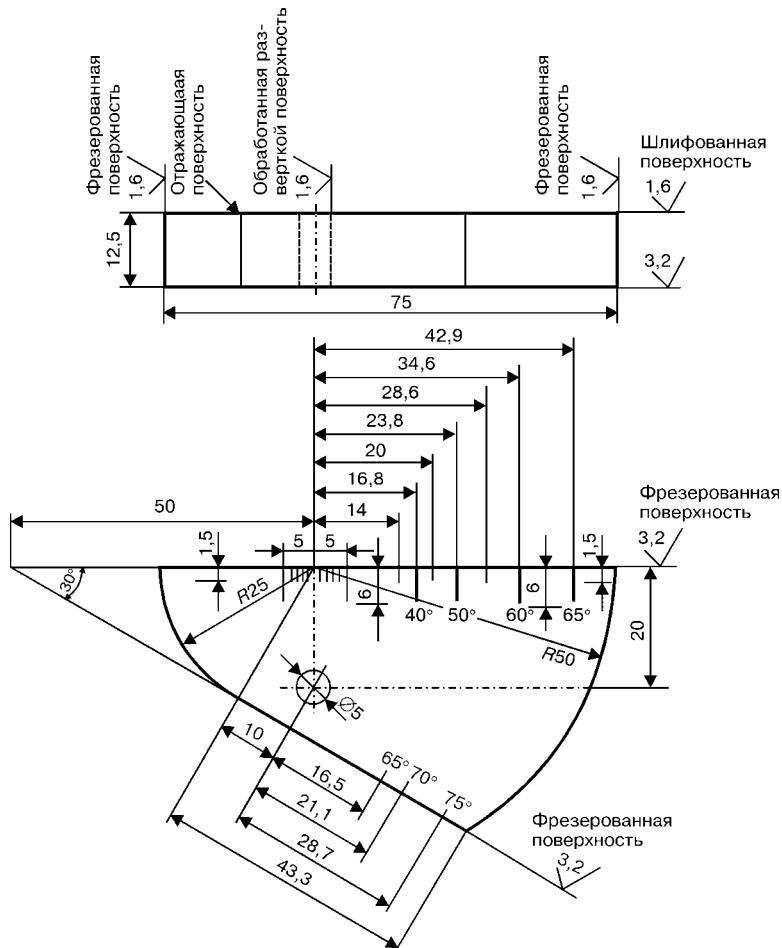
Калибровочный образец № 2 для УЗ контроля (V2)
